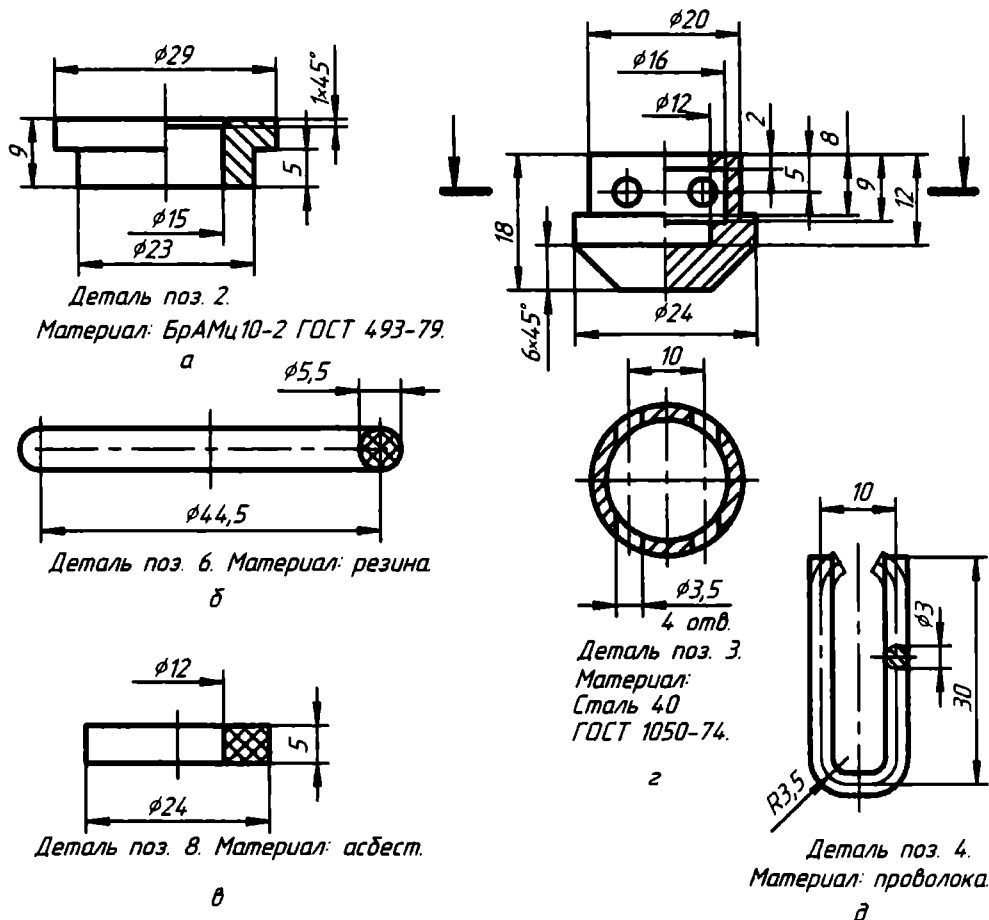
Чертежи: а — седла; б, в — уплотнительного кольца; г — клапана; д — скобы
